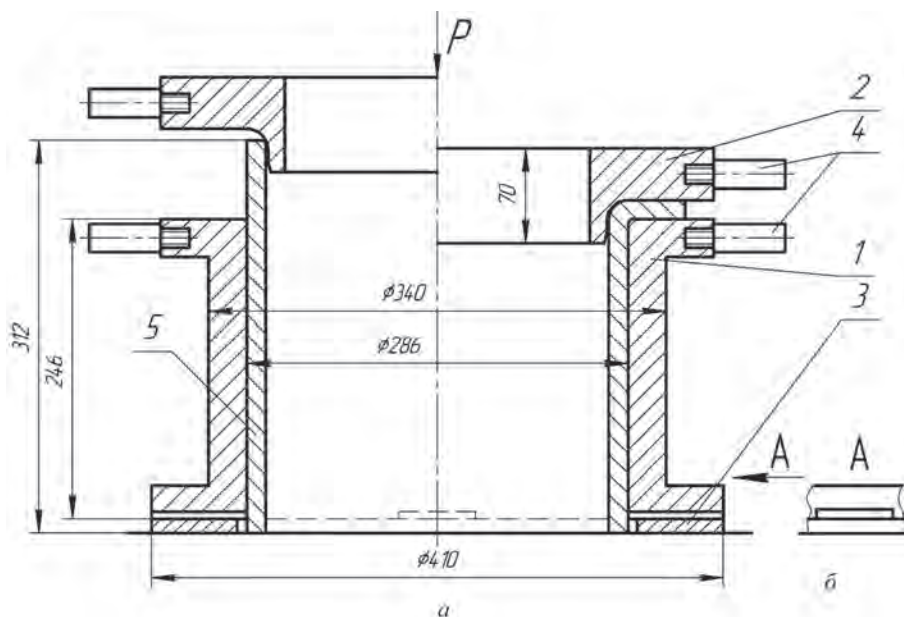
Схема штампа для моделирования процесса отбортовки промышленных образцов трубных заготовок
